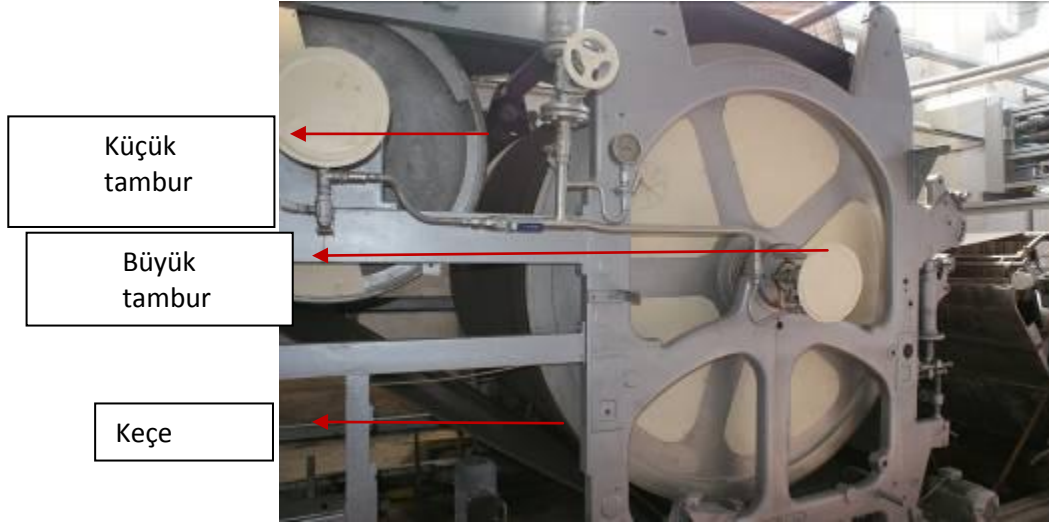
Kumaşın keçe blanket ile silindirlerin arasından geçişi
